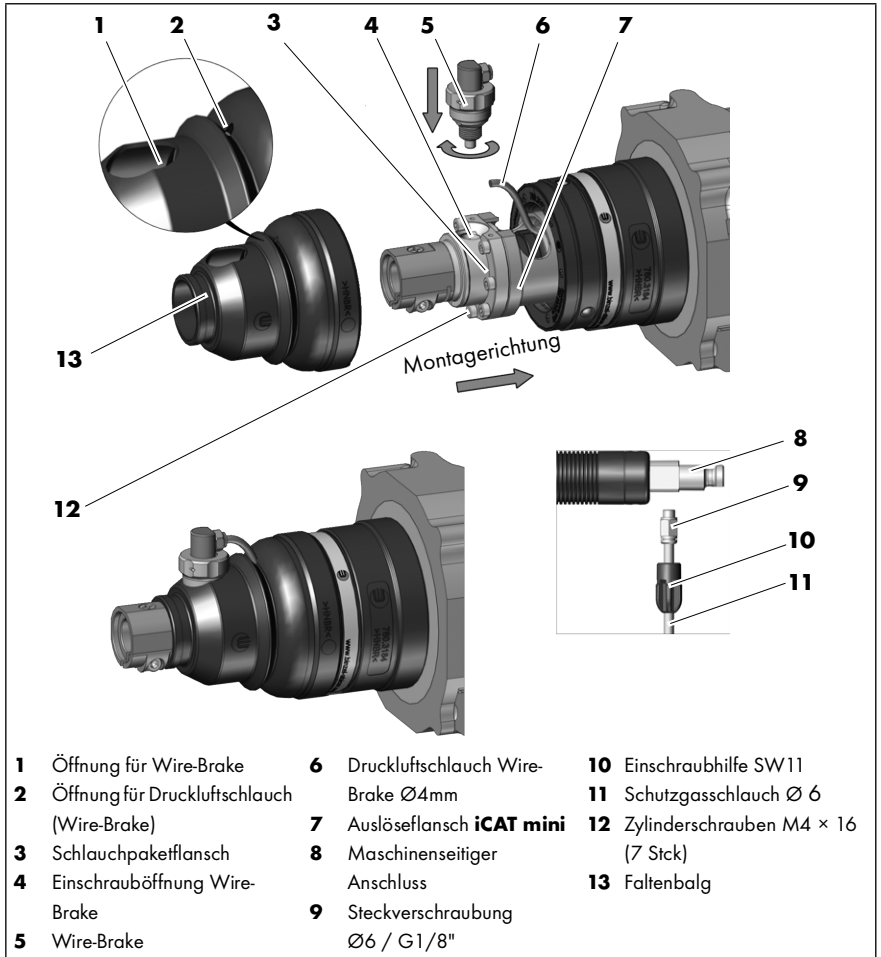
Schlauchpaket montieren – iCAT mini für ABIROB® G mit Wire-Brake
